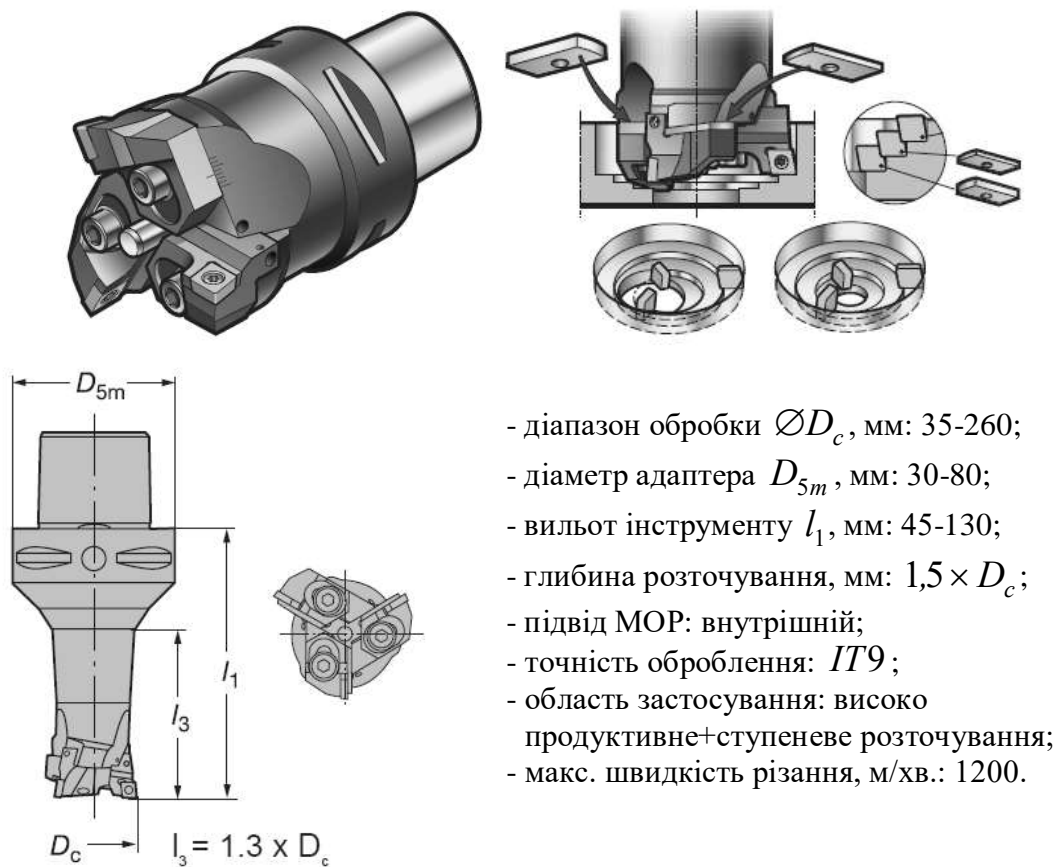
Інструмент для ступеневого розточування із трьома пластинами
